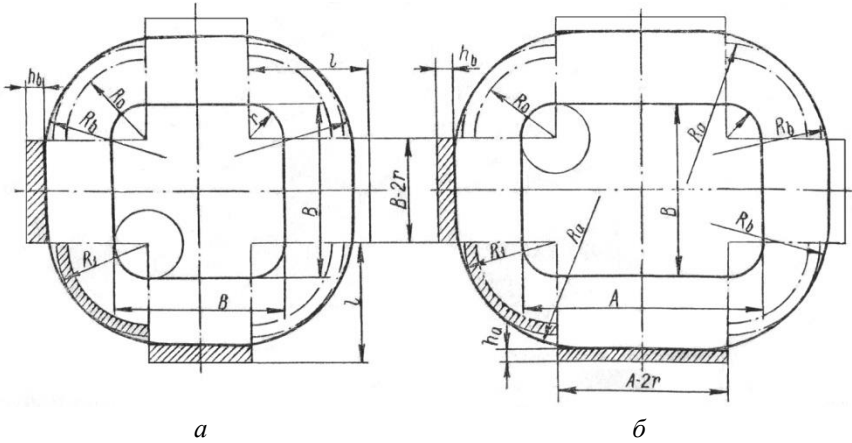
Побудова форми заготовки для витягування невисоких коробок з відносно великими радіусами кутових заокруглень (область IIb рис. 5.1): *a* – для квадратної; *б* – для прямокутної коробки
